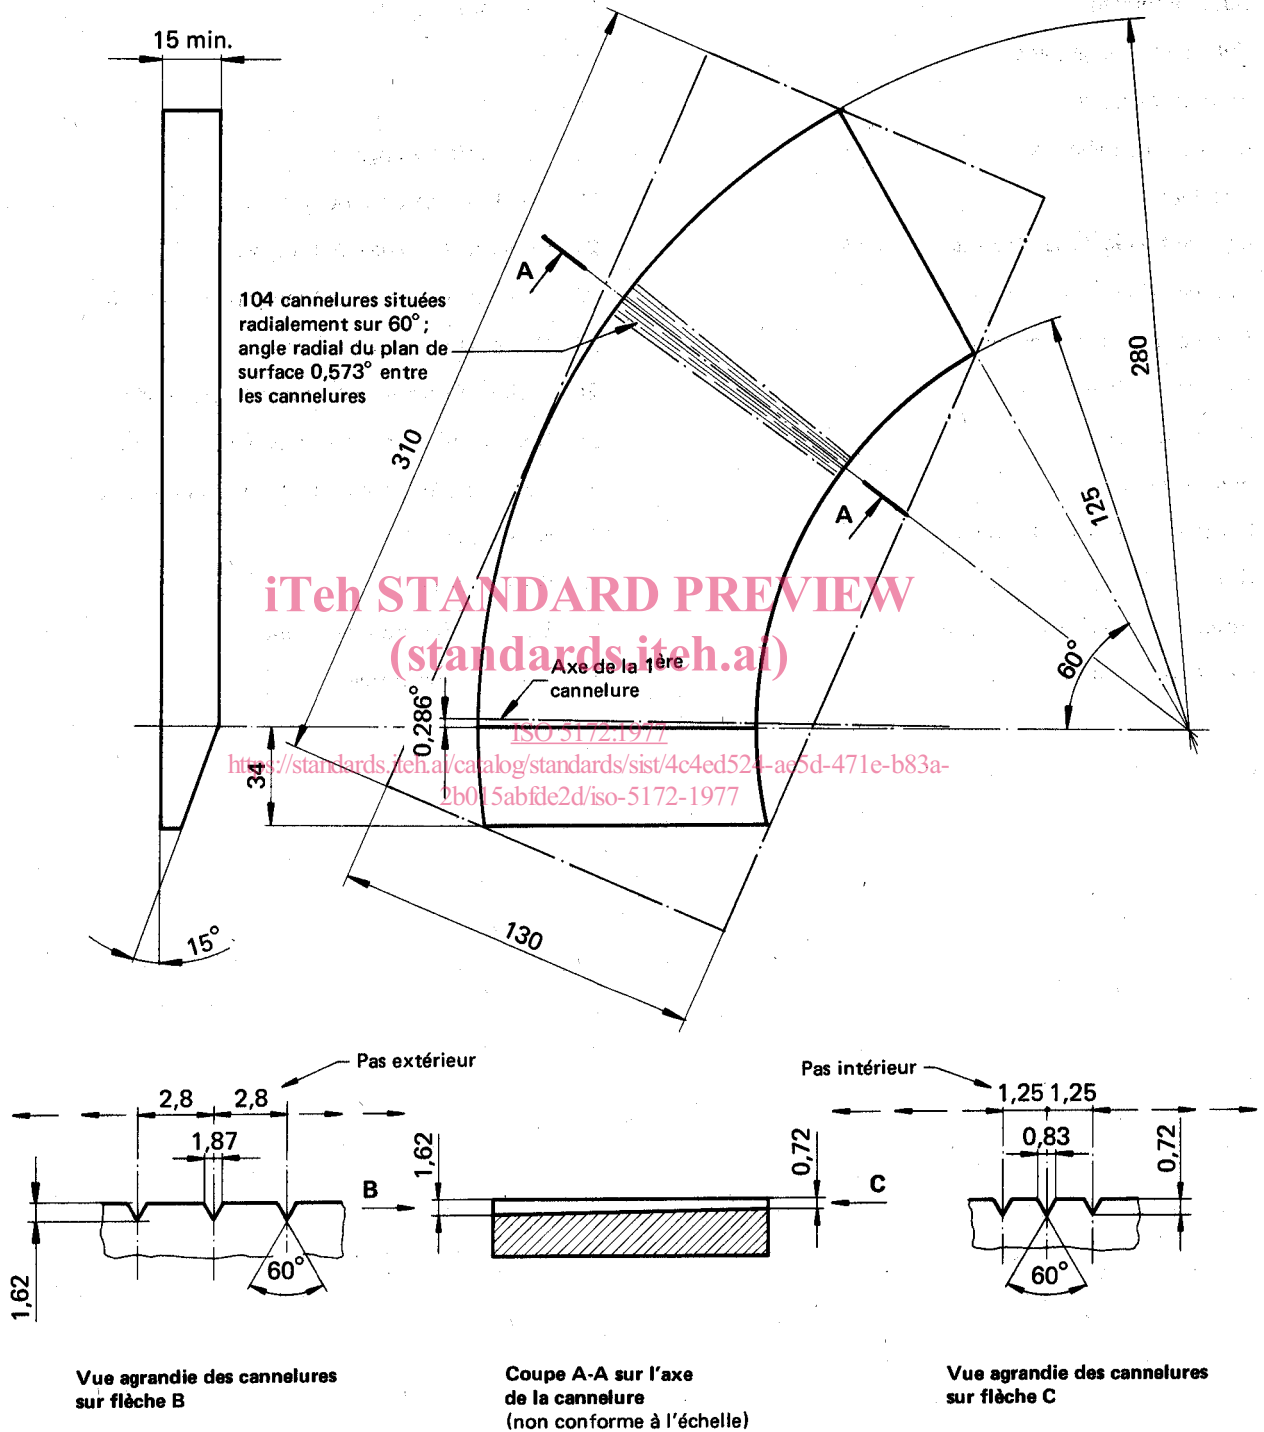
Dessin des pièces d'essai en cuivre cannelées par machine
